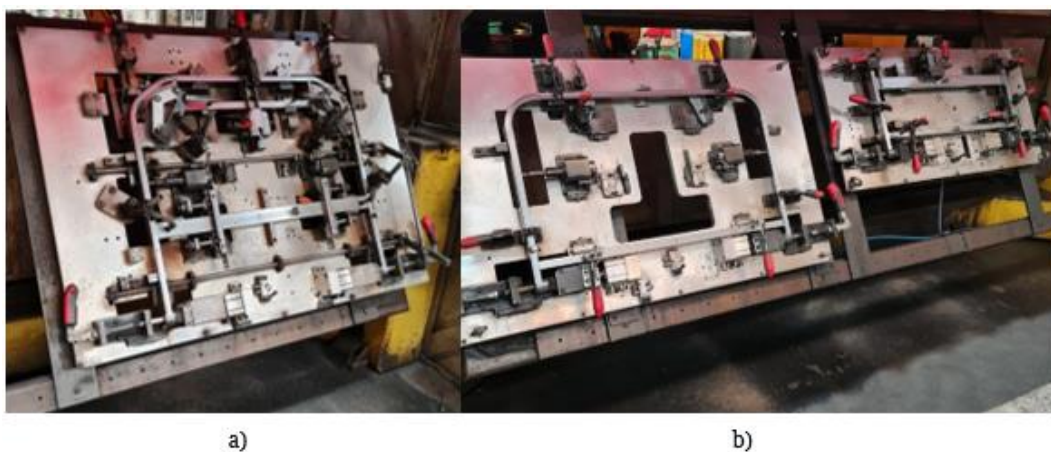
Gabaris de soldadura a) apoio para costas b) suporte para pés e secção de joelhos
